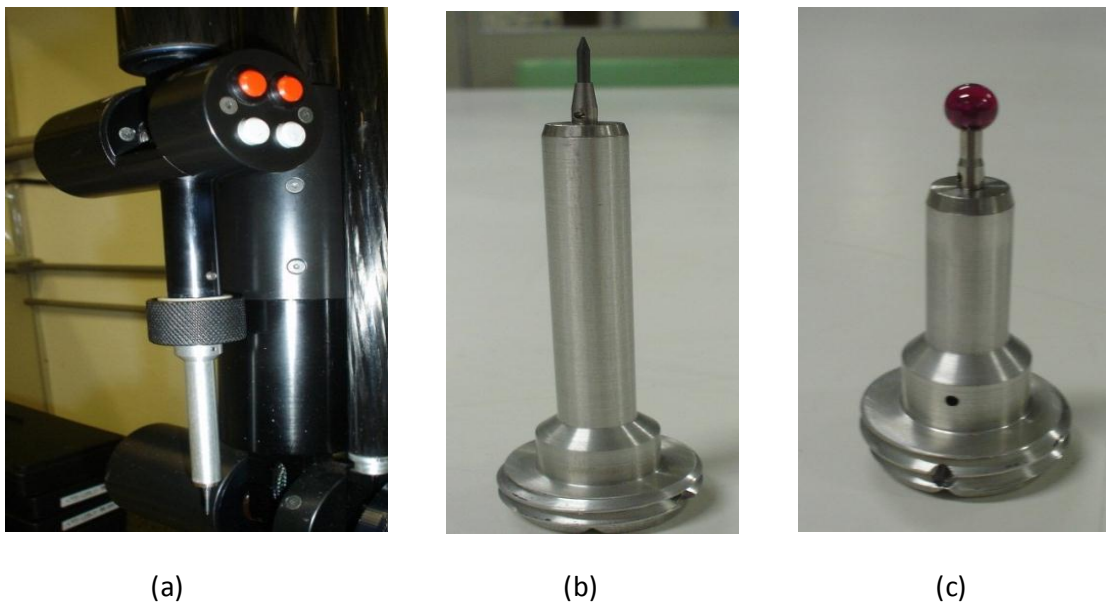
Tipos de Apalpador na MMC Braço Articulado, (a) Sonda de medição, (b) apalpador Ponta seca, (c) Apalpador esférico com 6 mm de diâmetro.
